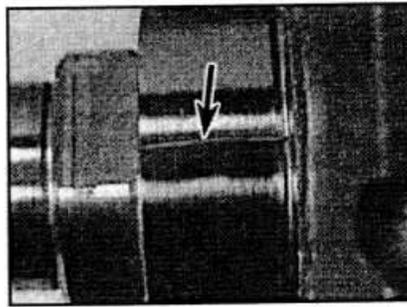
D.75. Расположение фирменного стержня Plastigage для измерения зазоров в коренных подшипниках.
